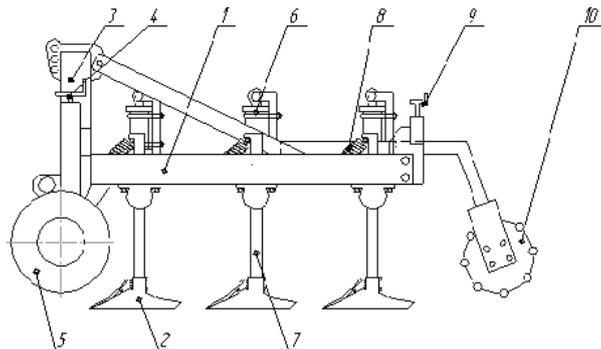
Культиватор КСТ-3,8 с прикатывающим приспособлением:
